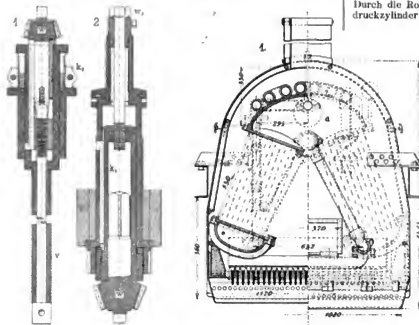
Z. A.: Zwinginfige Kesselsiedermaschine.
